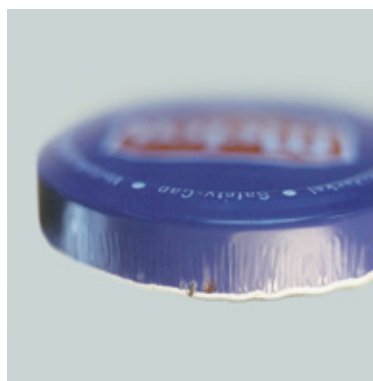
Krauser Rand bei Twist-Off Metallverschluss.
